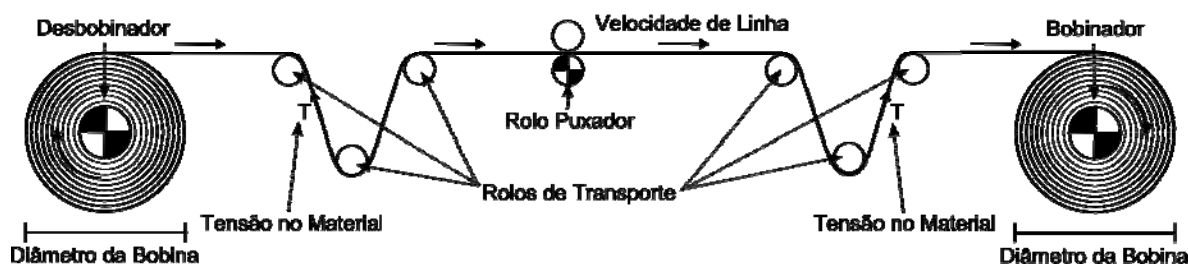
Identificação de termos utilizados em bobinadores e desbobinadores axiais
